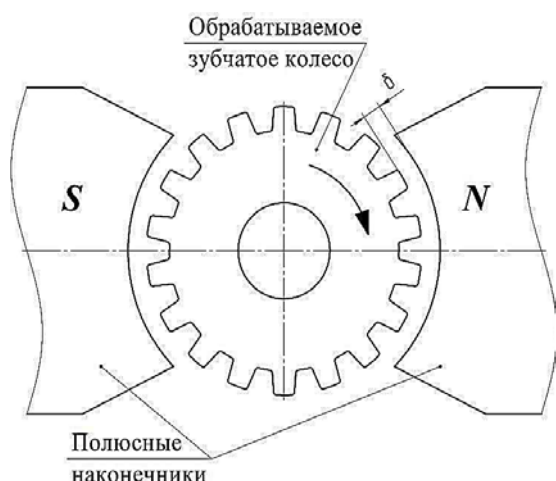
Схема магнитно-абразивной обработки мелкозубчатых цилиндрических зубчатых колес
